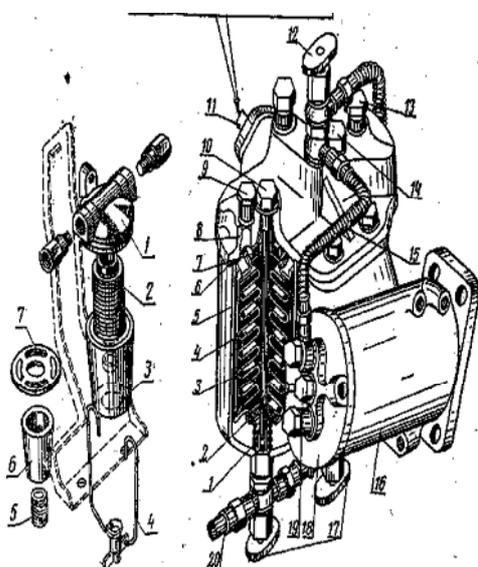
Фильтр тонкой очистки топлива двигателей СМД-62 и СМД-64: 1 — пружина; 2, 7 — сальники; 3 — стяжной болт; 4 — бумажный фильтрующий элемент; 5 — корпус; 6 — прокладка; 8 — крышка; 9, 13 — болты поворотных угольников; 10, 14, 19 — гайки; 11 — трехходовой кран; 12, 17 — вентили; 15 — трубка; 16 — фильтр-кронштейн; 18 — крышка; 20 — сливная трубка.
